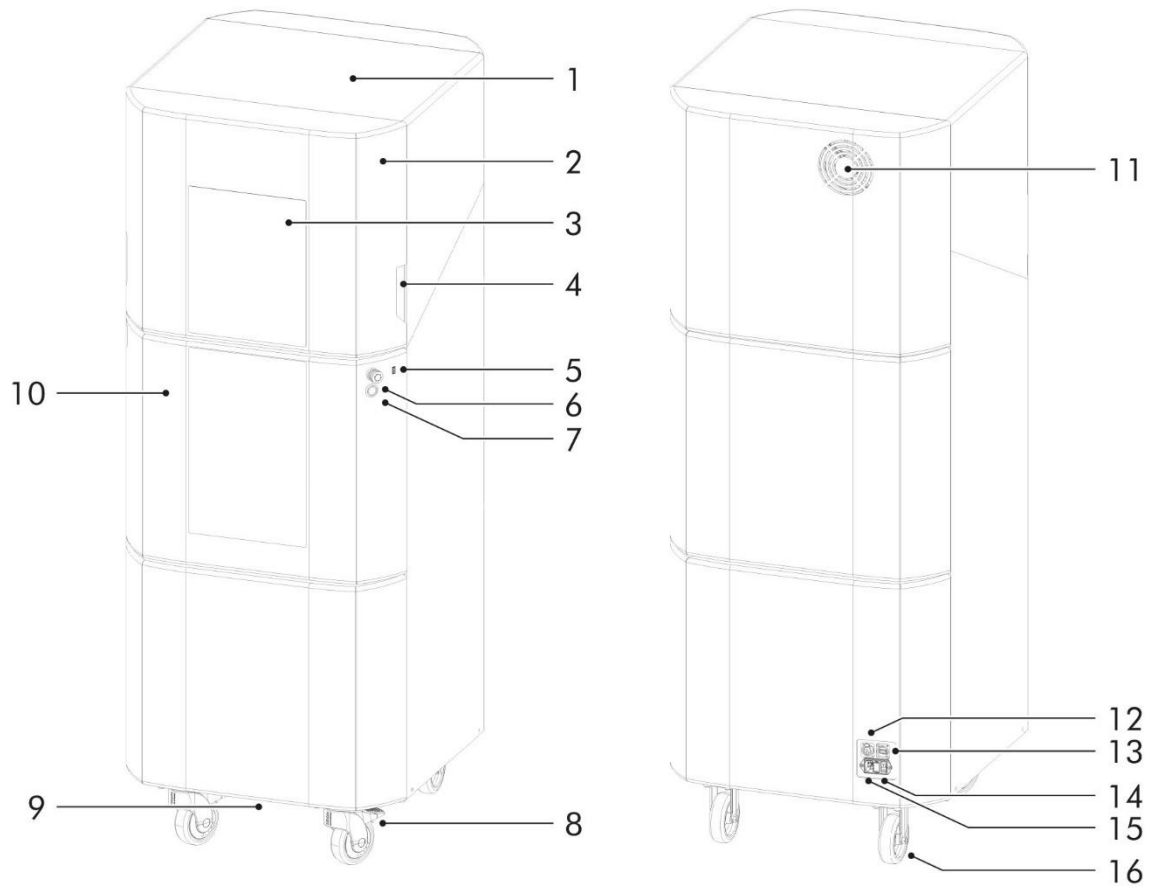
Vue d'ensemble de la machine, avant et arrière
